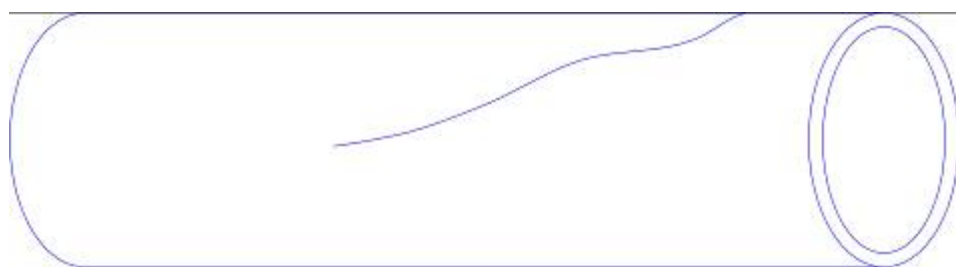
Сталеплавильная единичная плена, образующаяся при раскатывании наплыва на поверхности слитка и заготовки по протяженности значительно короче, чем на рисунке 2
